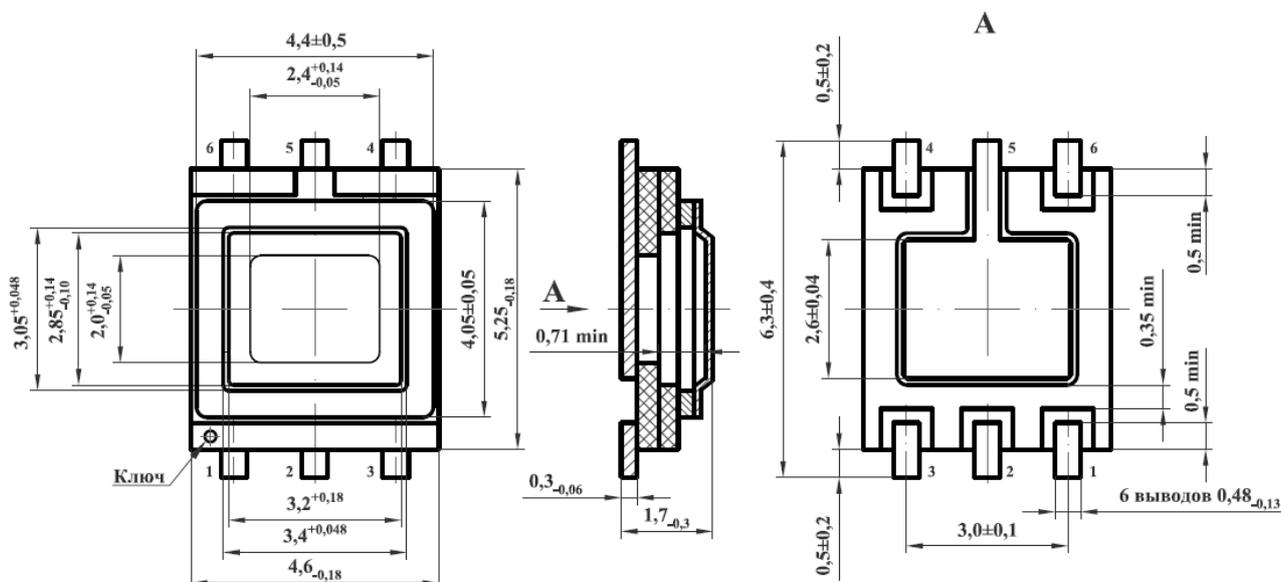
Габаритный чертеж корпуса 5221.6-1 (размеры в мм)
